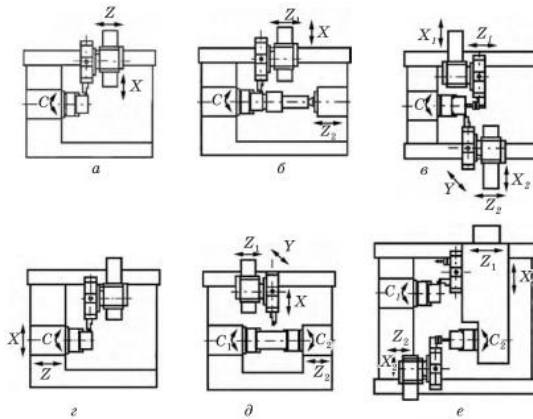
Компонувальні схеми верстатів токарної групи з горизонтальною віссю обертання деталі
